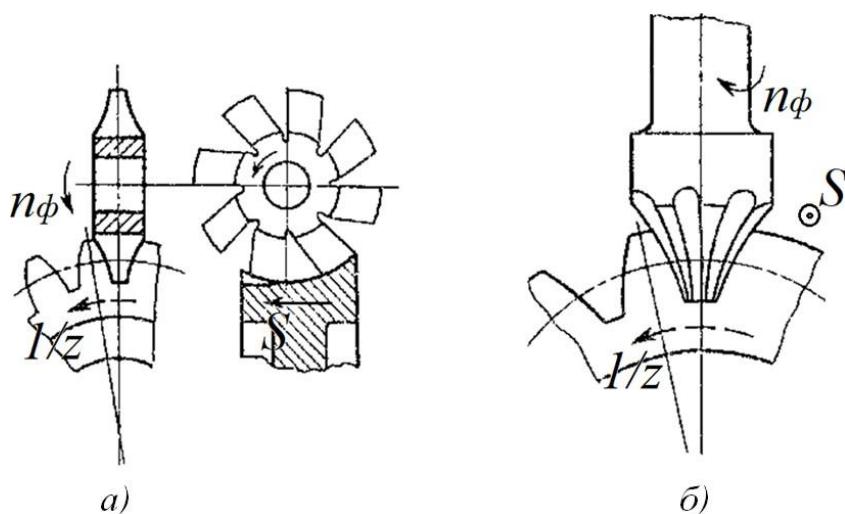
Схема нарізування дисковою і пальцевою фрезами [33]
